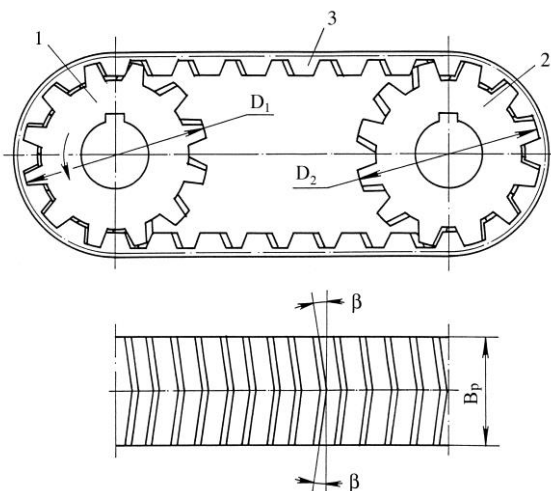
Конструкция зубчато-ременной передачи с шевронным зацеплением:
